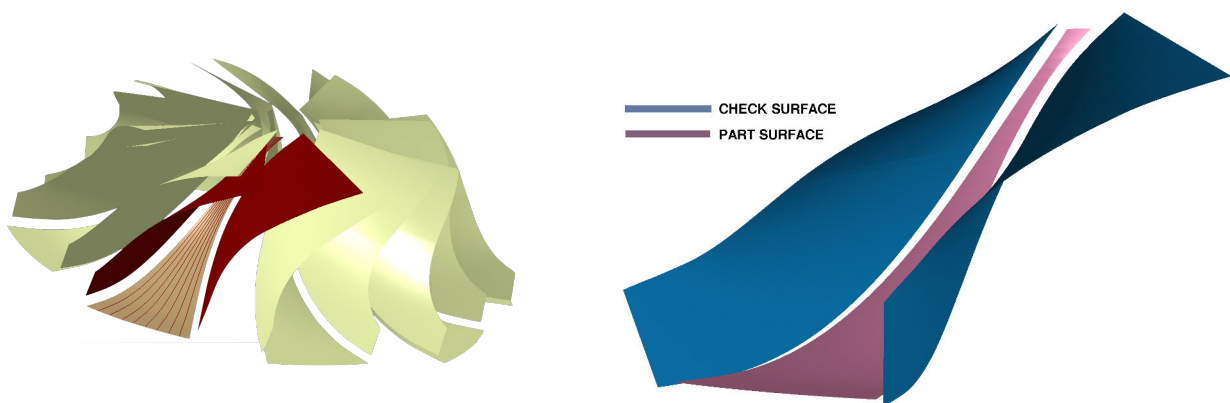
Pièce test et détail des surfaces pour la veine étudiée
